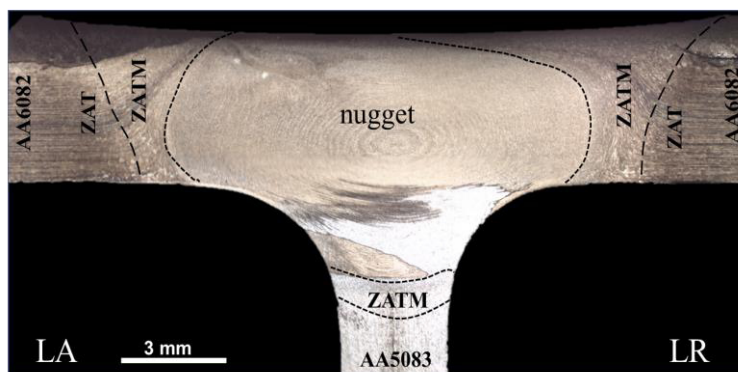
Diferentes zonas da microestrutura da soldadura DLPP-65-116
